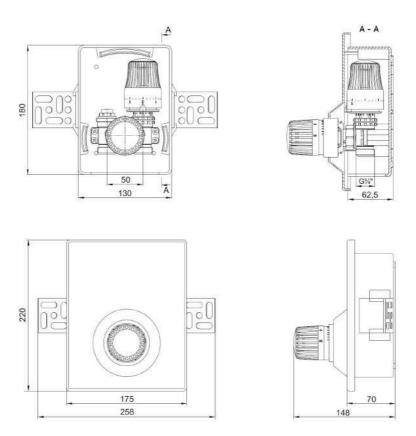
Габаритные размеры регулировочного короба Oks00728
